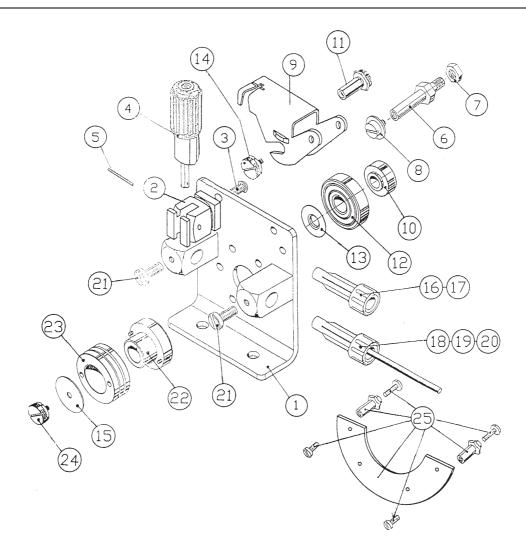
/5 а. 2-роликовый механизм подачи сварочной проволоки. Изображение в разобранном виде /exploded view wire feed 2-rolls drive
